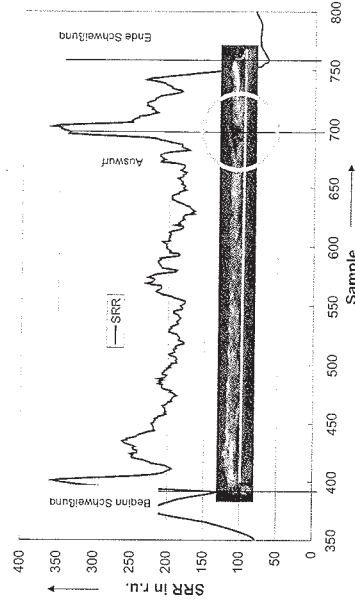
Auswürfe in Aluminium, gemessen mit dem Rückreflexsensor.
